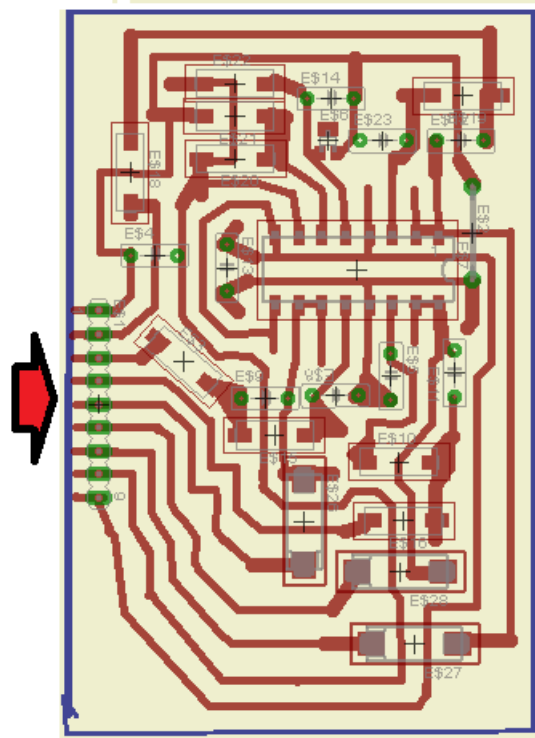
Placa PCB del geófono SAPOST (parte b).
